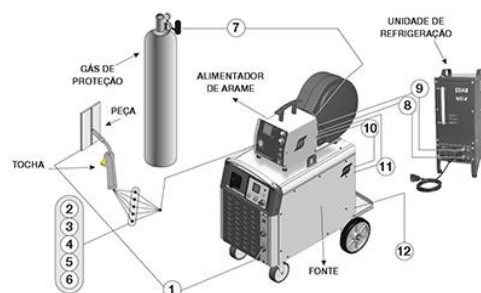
Esquema de soldadura MIG/MAG.
